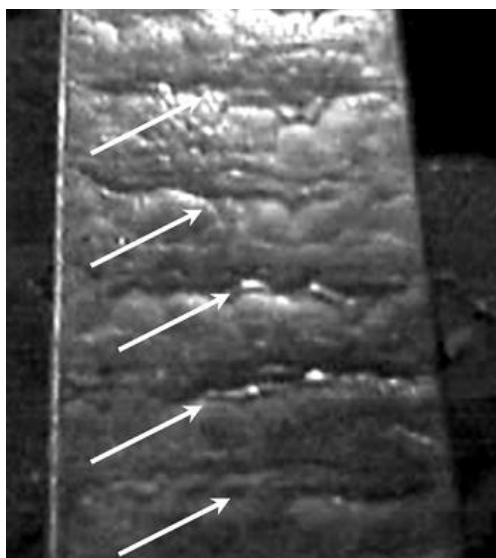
Наплывы на поверхности заготовки из-за микропрорывов в кристаллизаторе(подвисяния)
